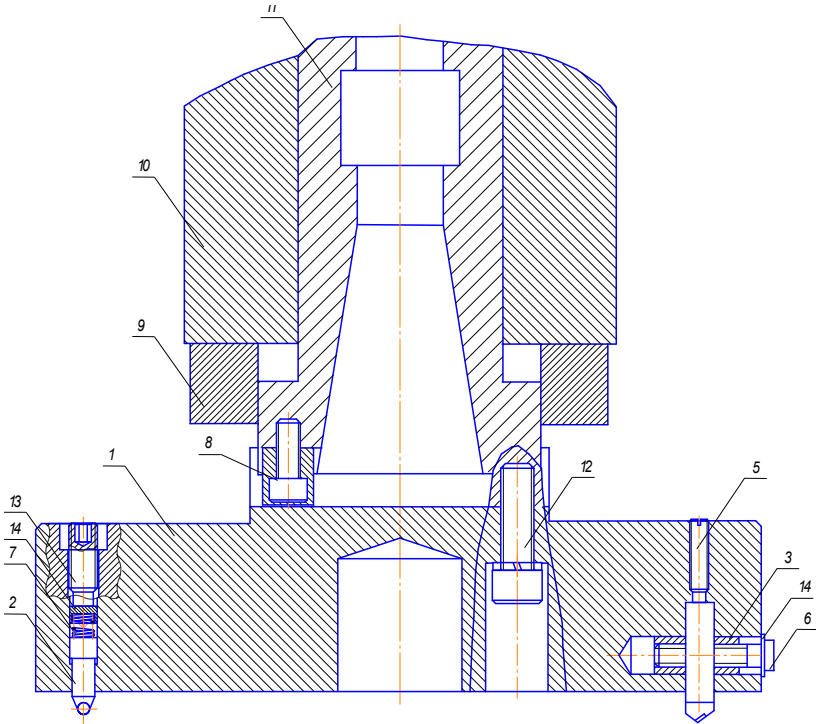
Конструкція торцевої фрези для реалізації запропонованої схеми обробки
